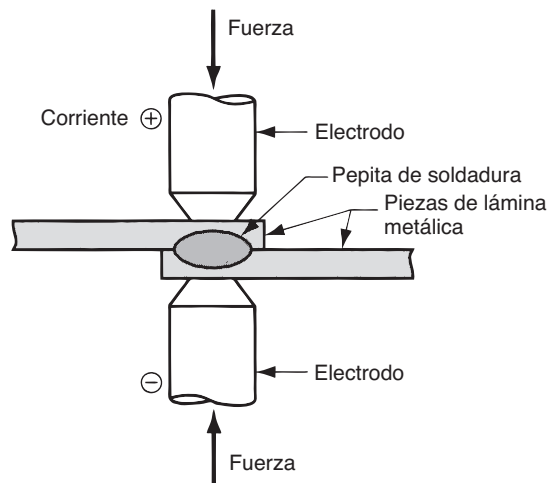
Soldadura por resistencia; se muestran los componentes en la soldadura de puntos; el proceso predominante en el grupo de RW.
